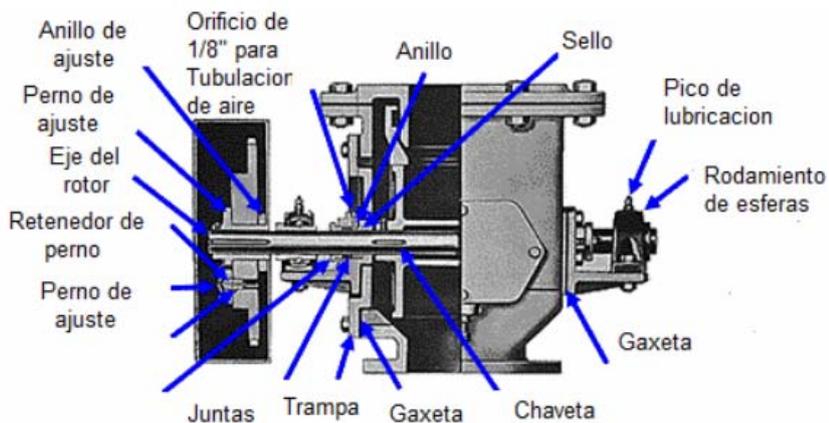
COMPONENTES INTERNOS DE VÁLVULA
